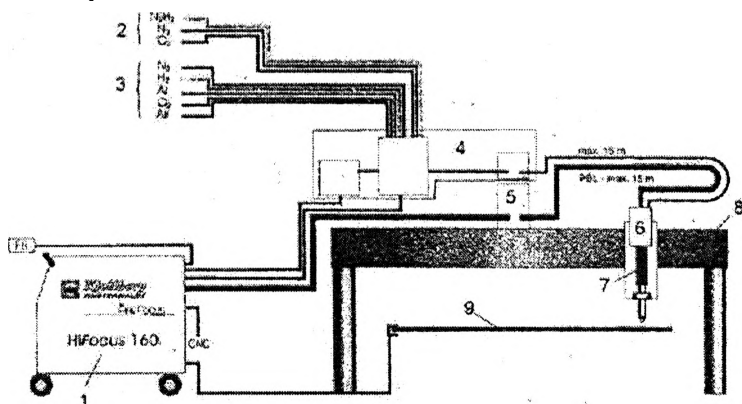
Схема современной механизированной установки для плазменной резки. 1 – источник тока; 2 – вихревые газы; 3 – плазмообразующий газ; 4 – газовая консоль; 5 – устройство промежуточного поджига; 6 – устройство подключения плазматрона; 7 – плазматрон; 8 – портал машины тепловой резки; 9 – разрезаемый лист (заготовка)
